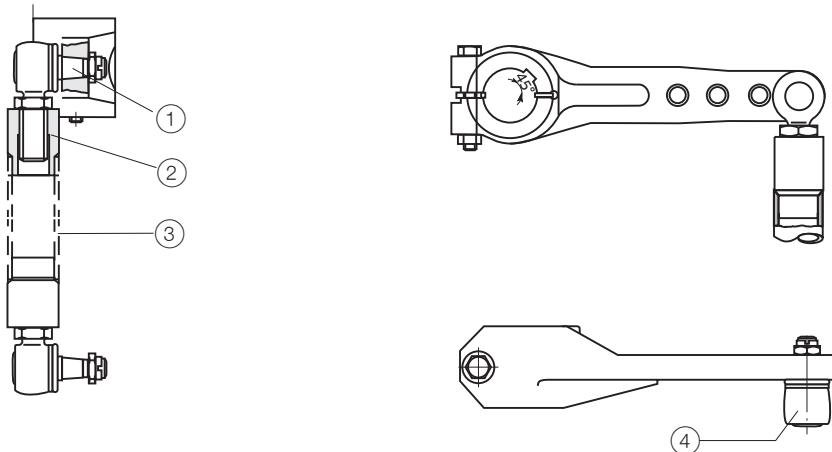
Компоненты соединительной тяги и размеры соединительной трубы
